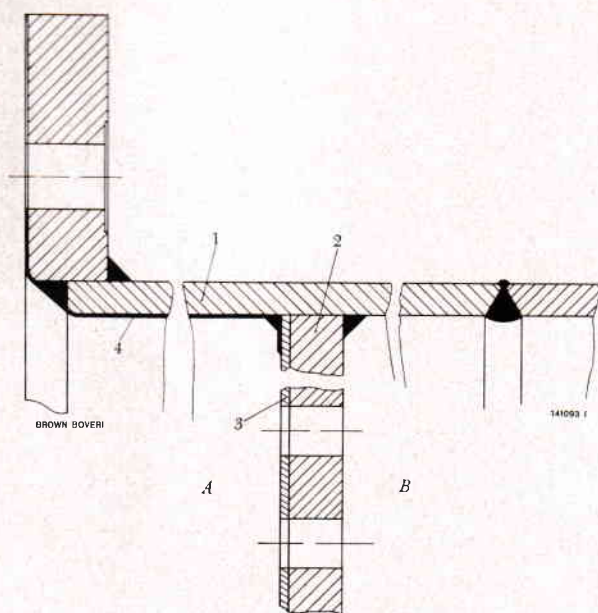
Boîte à eau en construction soudée avec plaque tubulaire soudée et couche protectrice sur le côté eau
